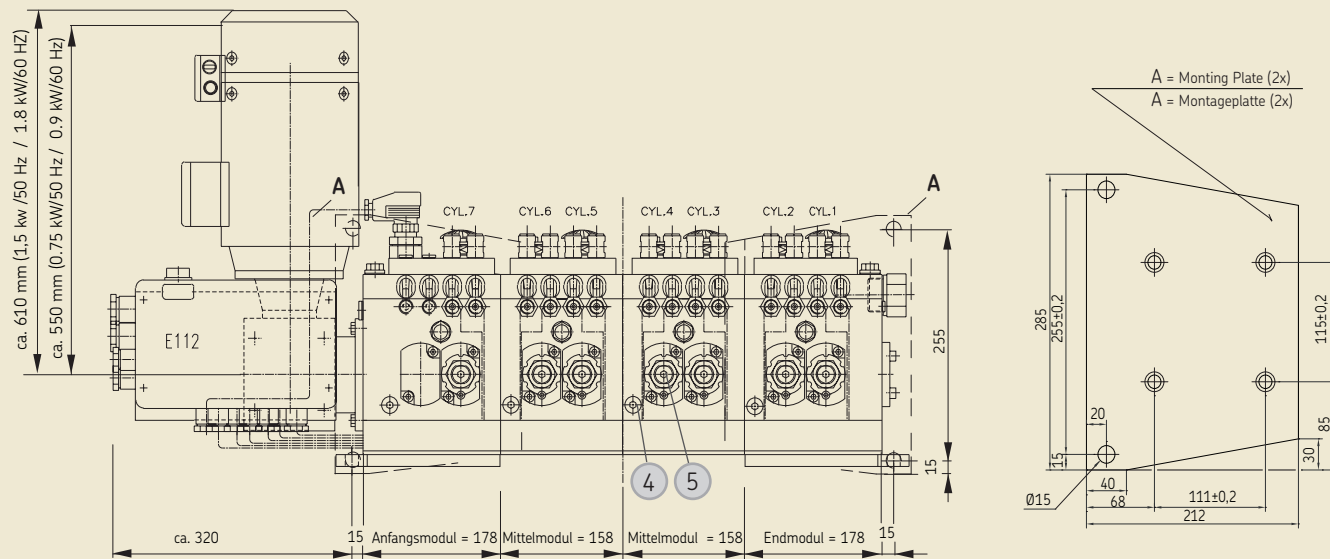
Montagezeichnung PC Ölschmierpumpenaggregat mit Elektromotor, Draufsicht mit Seitenansicht
